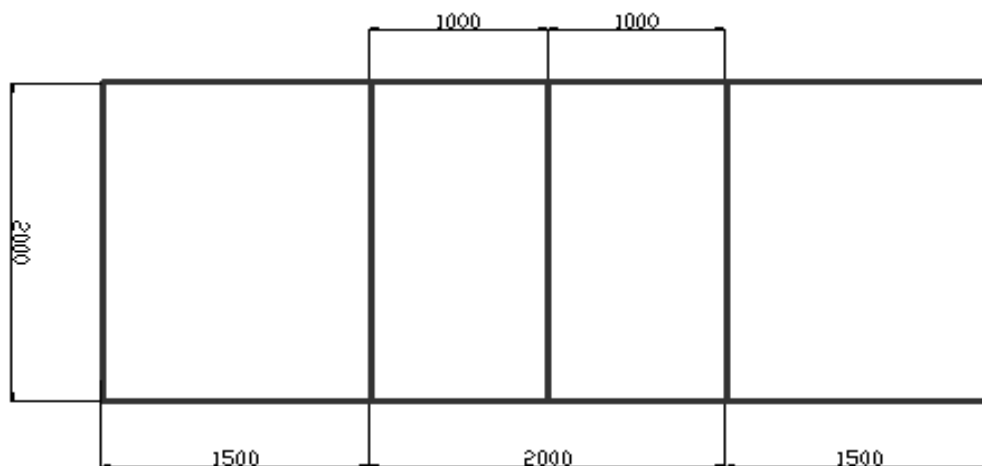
Diseño estructural de la bancada de deslizamiento. Vista superior.
